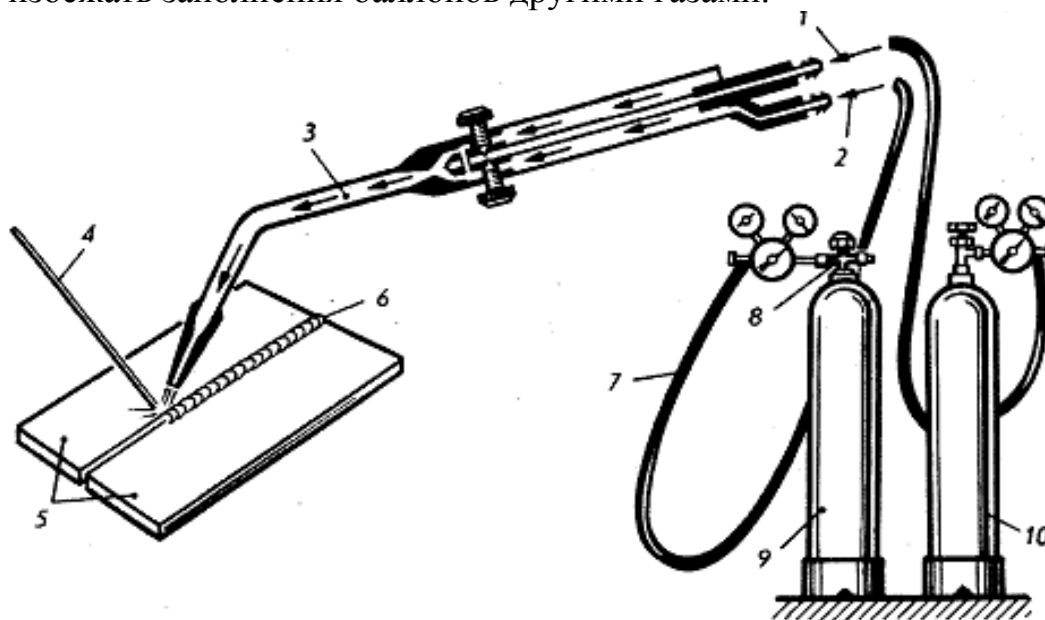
Схема поста газовой сварки листовых заготовок:
